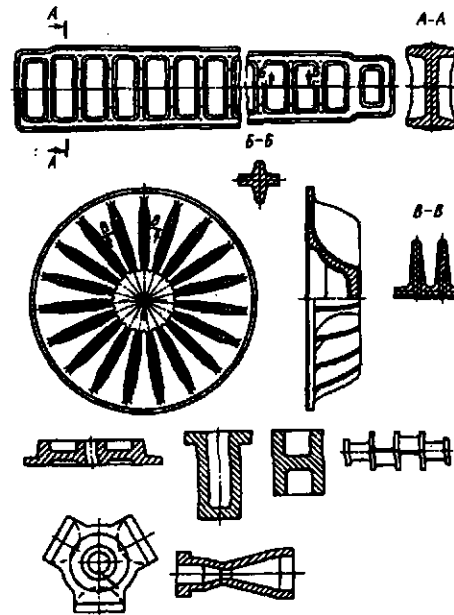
Штампованные заготовки, получаемые на гидропрессах
